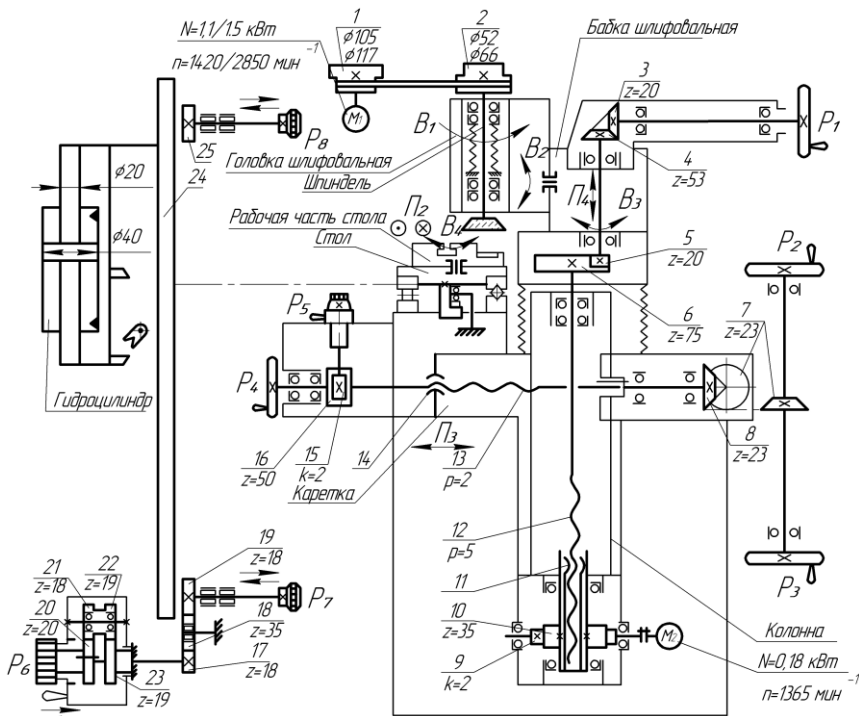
Кинематическая схема универсально-заточного станка модели 3Д642Е
